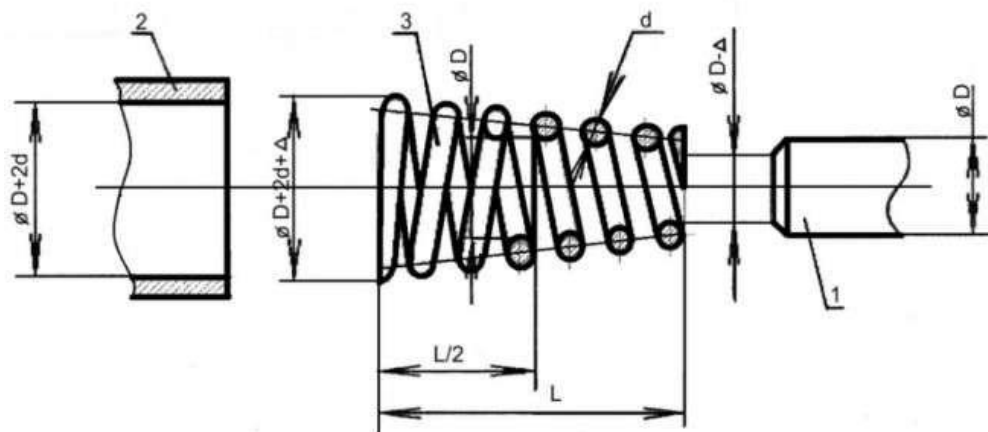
Конічний підшипник ковзання для зворотньо-обертального руху
